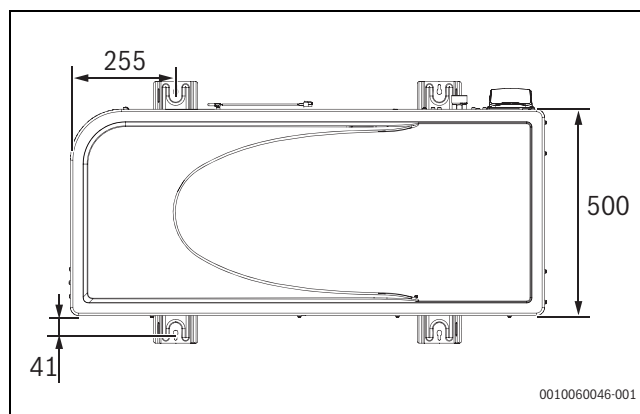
Dimensions de la pompe à chaleur, vue de dessus
